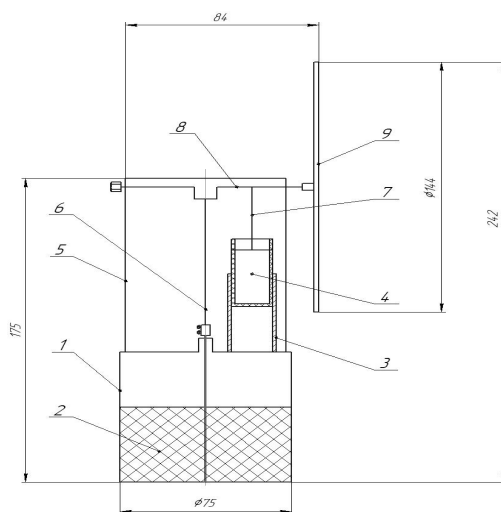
Схема установки: цилиндр; 2 — вытеснитель; 3 — рабочий цилиндр; 4 — рабочий поршень; 5 — корпус крепежа коленвала; 6 — тяга вытеснителя, закрепленная на эксцентриках; 7 — тяга (шатун) рабочего поршня; 8 — коленвал; 9 — маховик
